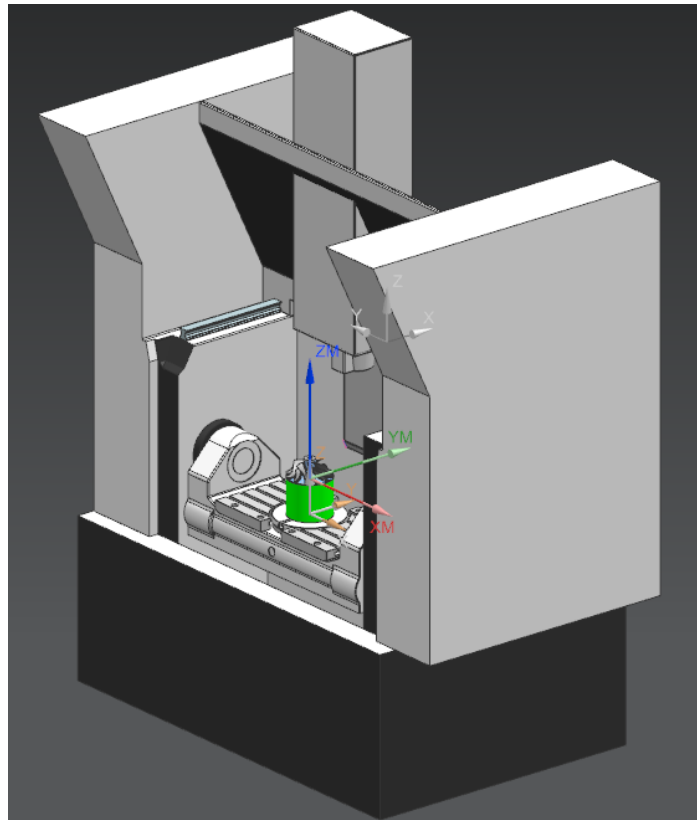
Montaje del impeller en la máquina CNC mediante NX 12.
